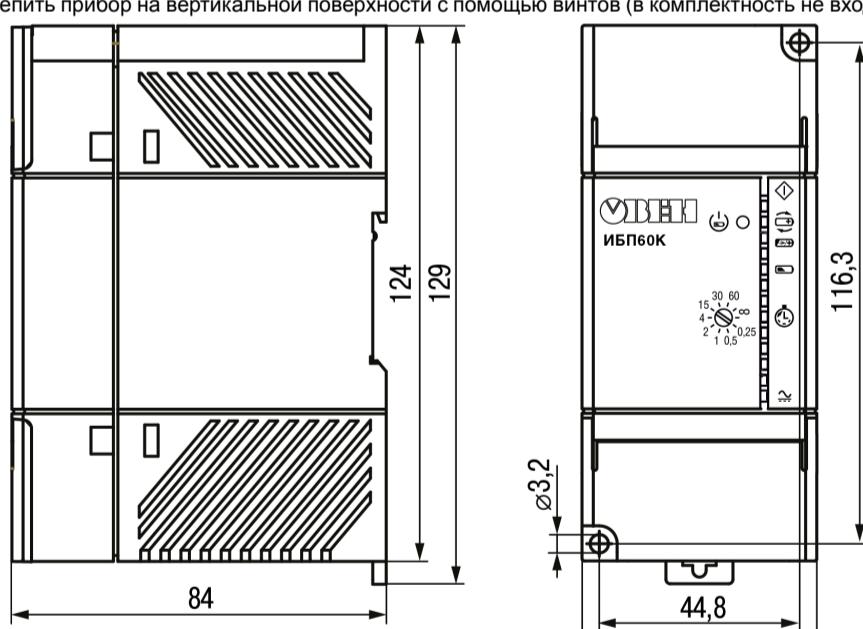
Внешний вид, габаритные и установочные размеры прибора
